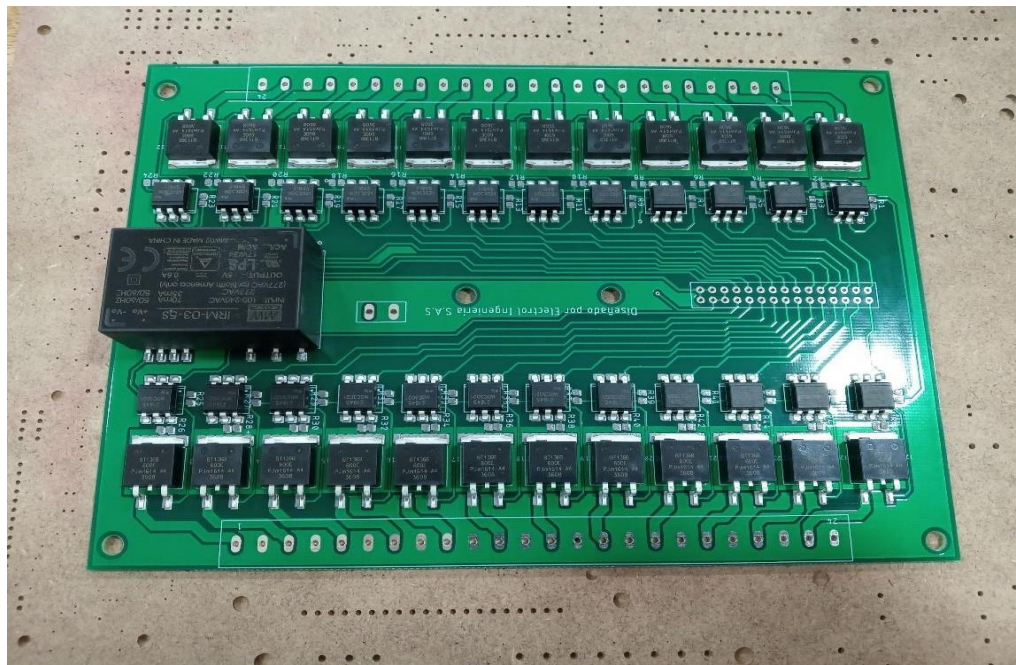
Componentes SMD soldados en tarjeta PCB AC. Tobón. (2019)
